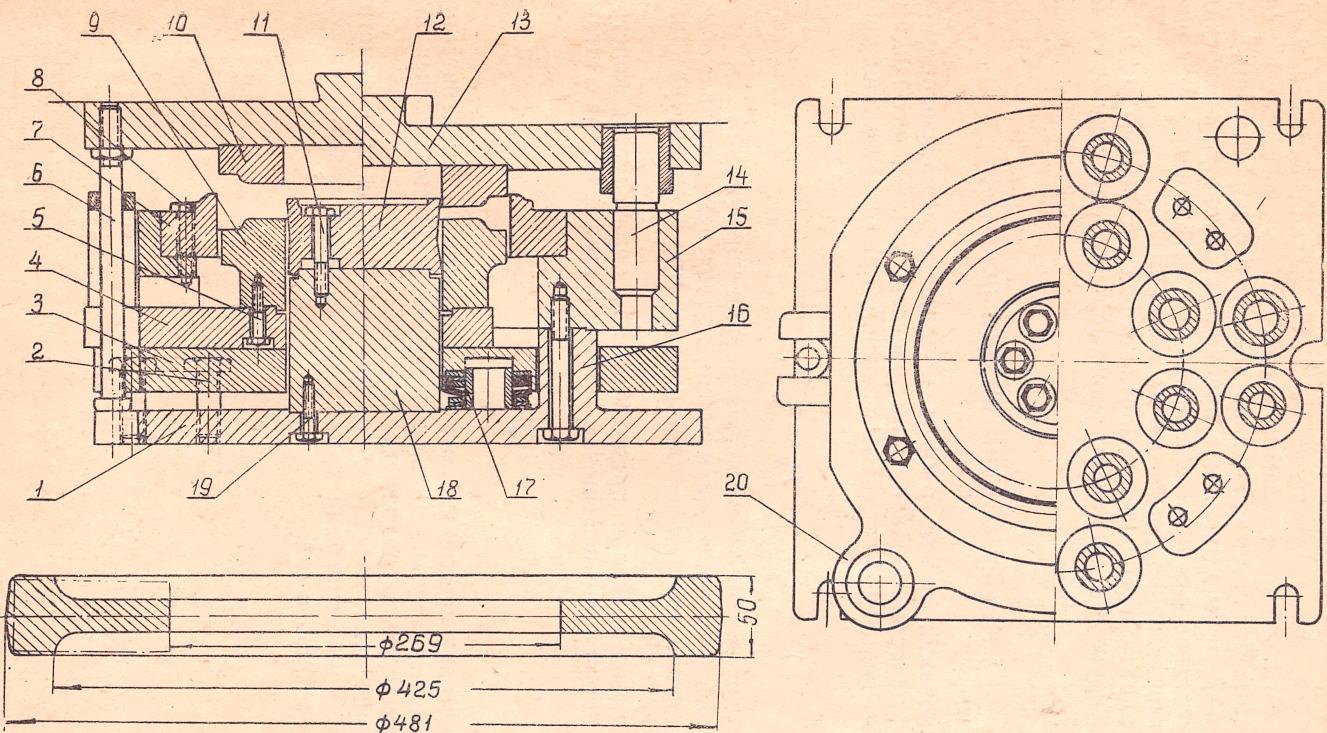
Штамп комбинированный для обрезки облся, прошивки пленки и правки поковки венца ведомой шестерни.
